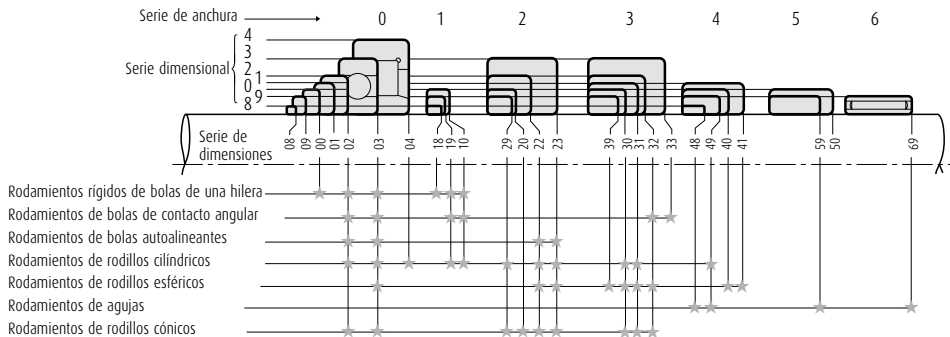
Series de dimensiones de los rodamientos radiales
